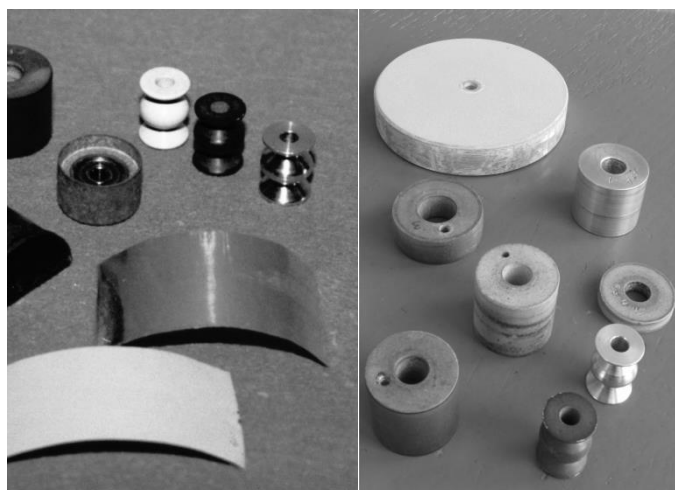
Образцы с покрытием и заготовки для нанесения покрытий.
